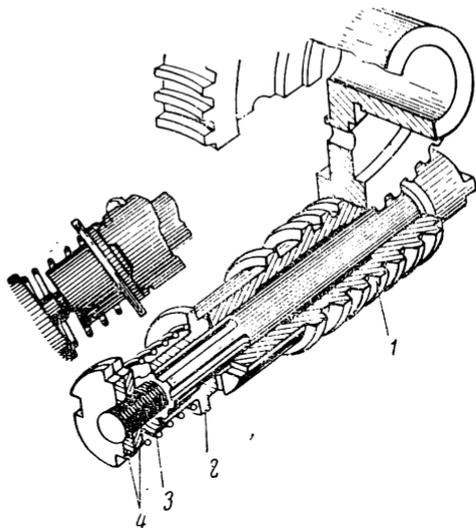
Предохранительный механизм привода подачи вертикально-сверлильного станка модели 2135
